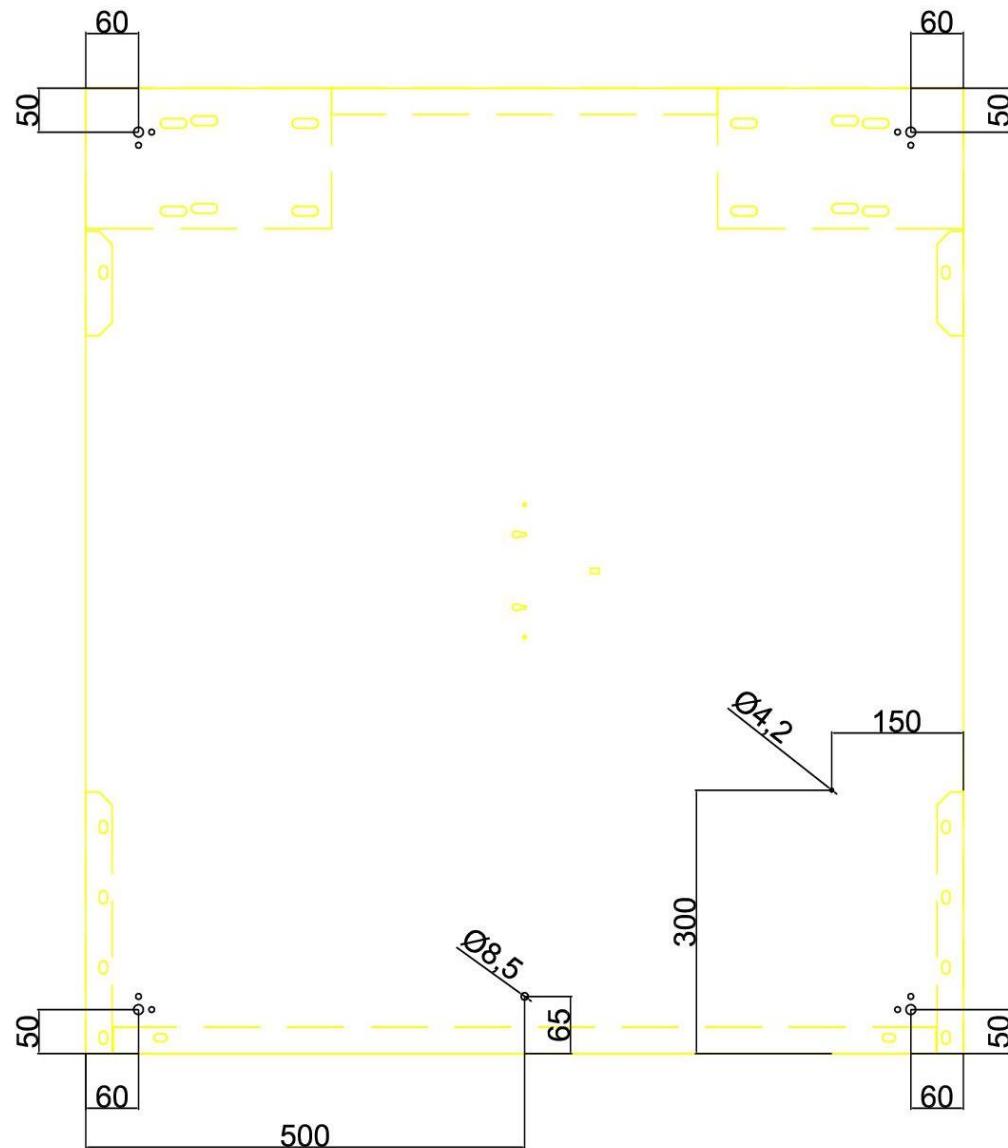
«Разметка и сверление отверстий под ввод кабеля и клемму заземления 400 кг»
